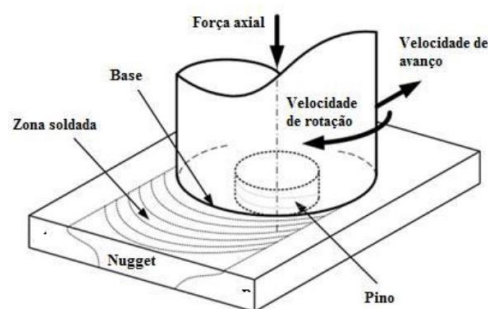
Principais parâmetros do processo de soldadura por fricção linear.
